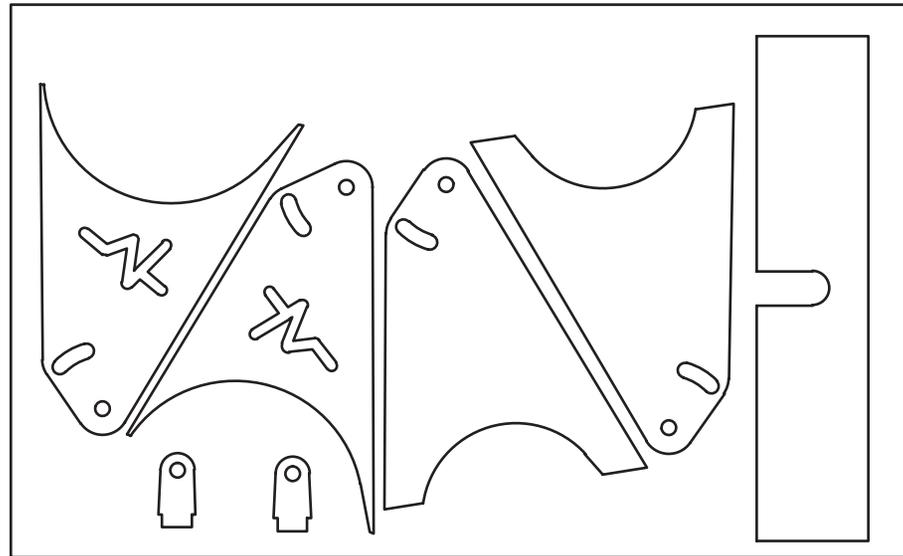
Cubicación en acero 304 de 1.5 mm (1:2)
